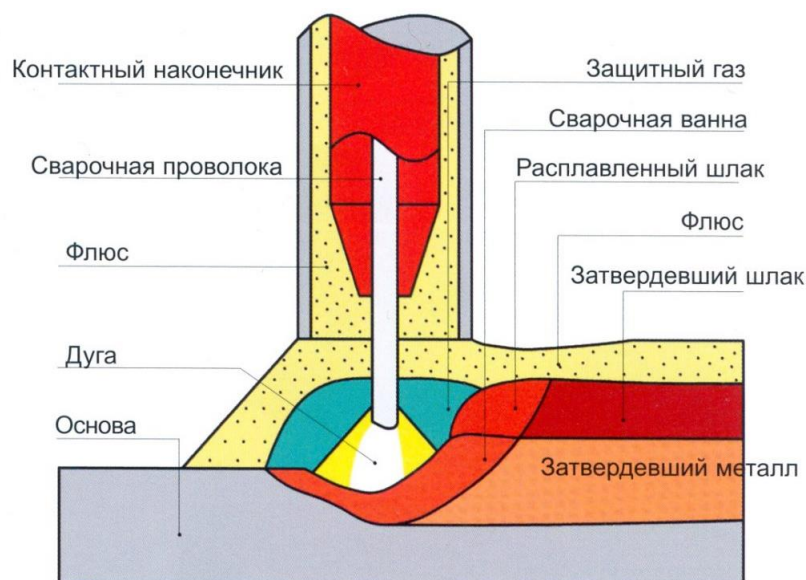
Схема автоматической сварки под флюсом
